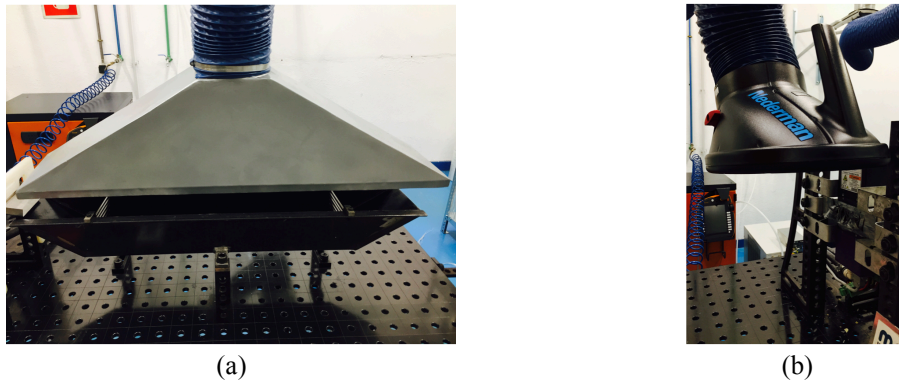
Sistemas de extracción: (a) sistema de extracción bañera; (b) sistema de extracción zona curado.
